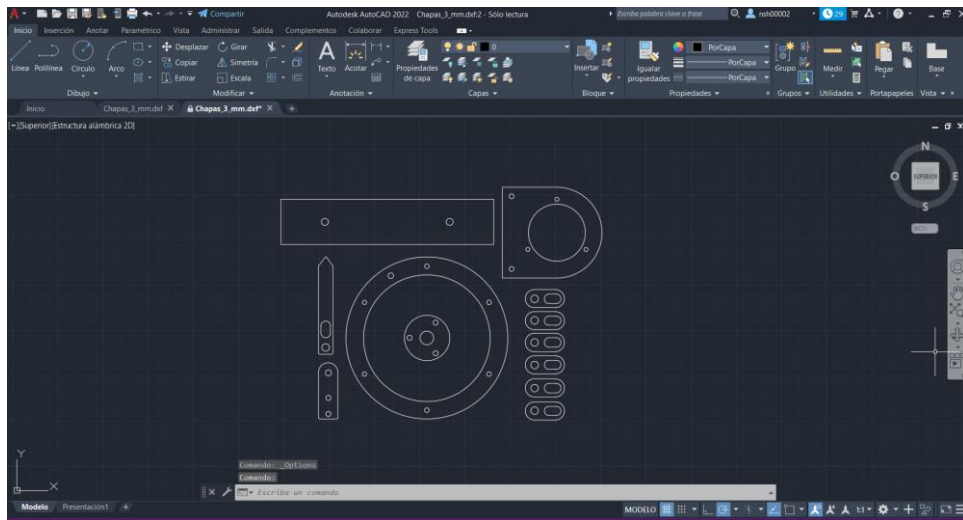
Chapas de aluminio de 3 milímetros para ser cortadas en la máquina de corte por agua
